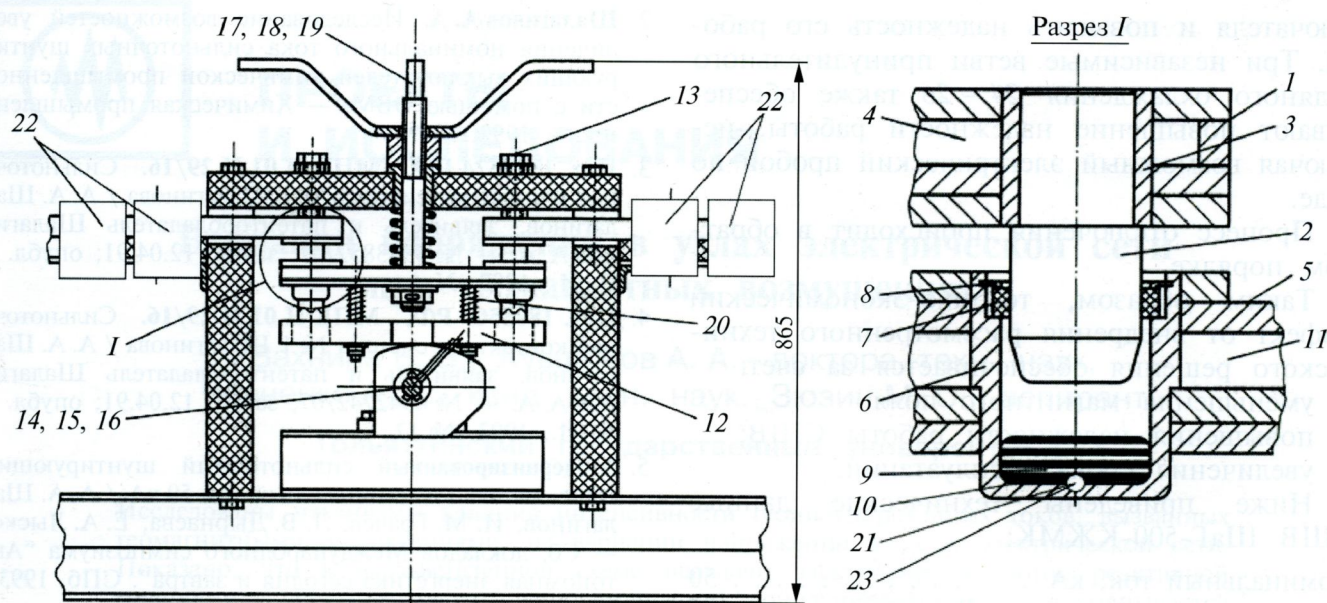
Сильноточный шунтирующий выключатель с композиционными жидкометаллическими контактами и системой принудительного водяного охлаждения ШаГ-500-КЖМК на номинальный ток 50 кА
